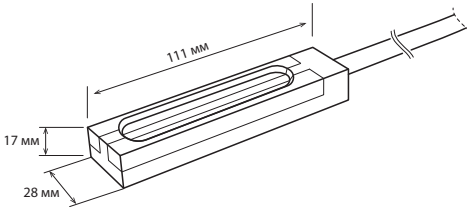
Габаритные размеры датчика кровли Ридан Roof 850RG
